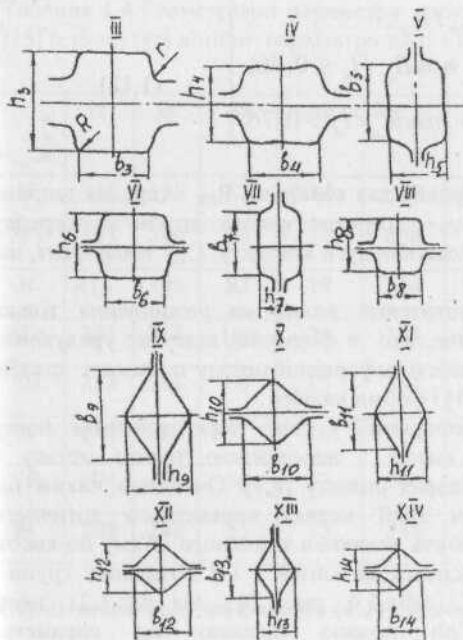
Схема калібрування валків неперервно-заготовочного стану (ящичні калібри перших двох клітей не показані)
